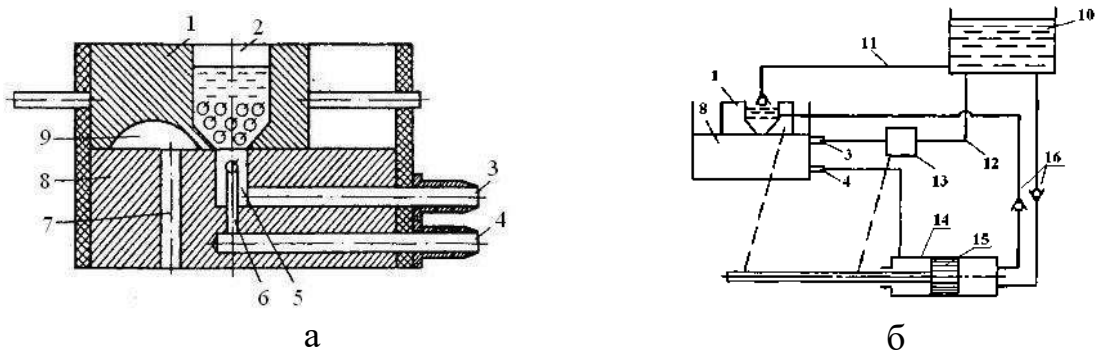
Пристрій для висіву пророслого насіння: а – висівна частина; б – структурна схема пристрою; 1 – верхня частина корпусу; 2 – бункер; 3, 4, 5, 9 – канали висівного апарату; 6 – трубка; 7 – насіннепровід; 8 – нижня частина корпусу; 10 – резервуар; 11, 12 – трубопроводи; 13, 16 – клапани; 14 – циліндр; 15 – поршень;
